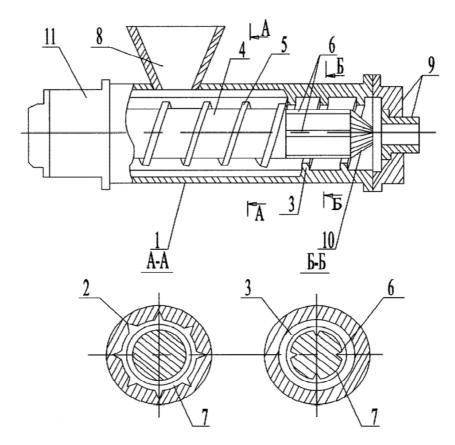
Шнековый экструдер по патенту РФ 2306775 [21]: 1 – корпус; 2, 6 – направляющие канавки; 3, 5 – винтовая нарезка; 4 – шнек; 7 – кольцевой зазор; 8 – загрузочное устройство; 9 – матрица; 10 – разрыхляющая насадка; 11 – привод
